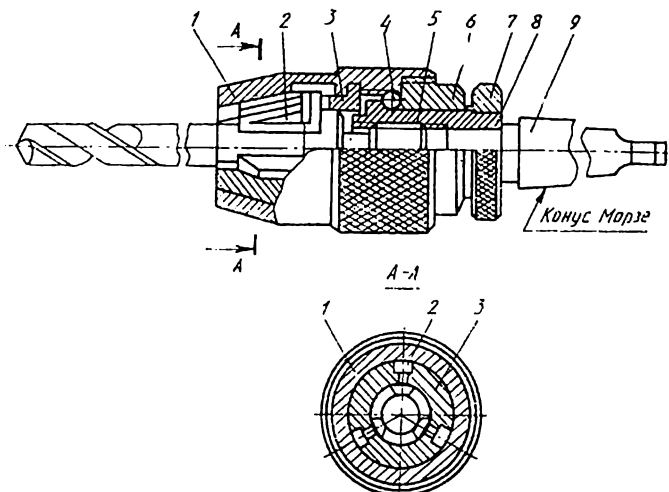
Трьохкулачковий безключовий свердильний патрон
